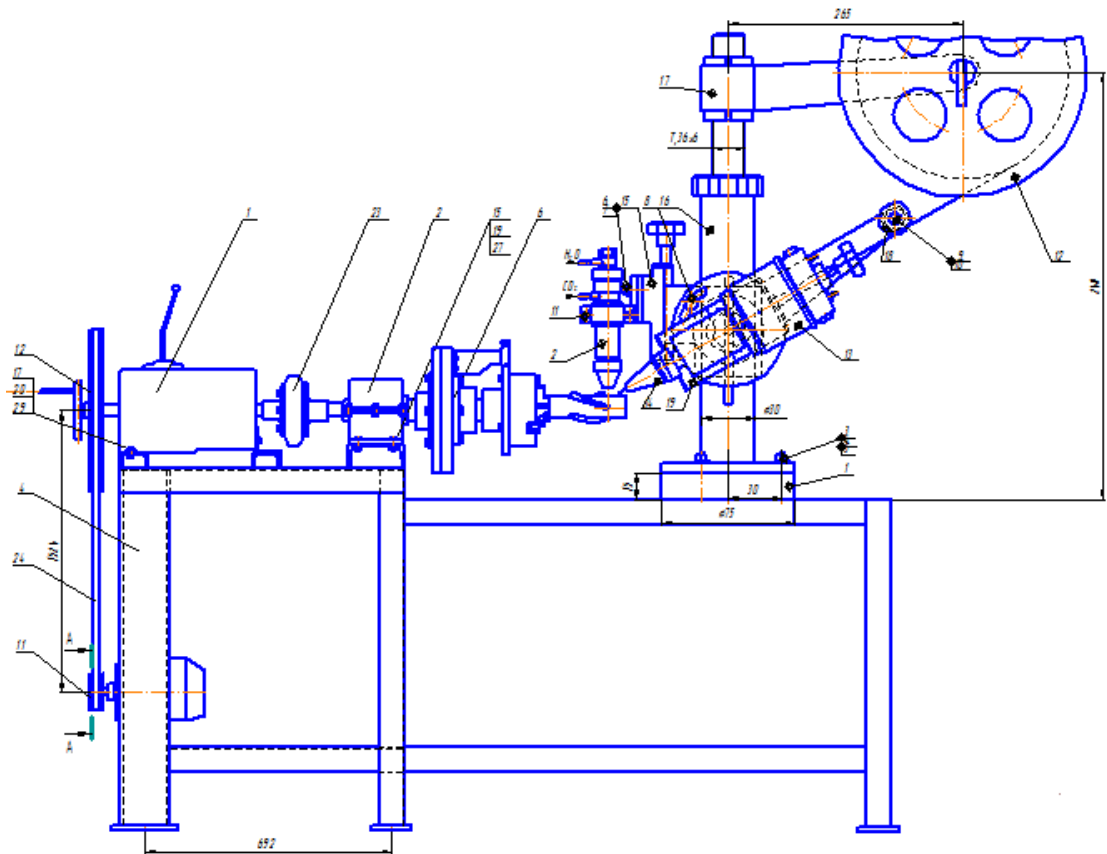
Стенд для обертово-поступального переміщення та зварювання лопаткового центратора
